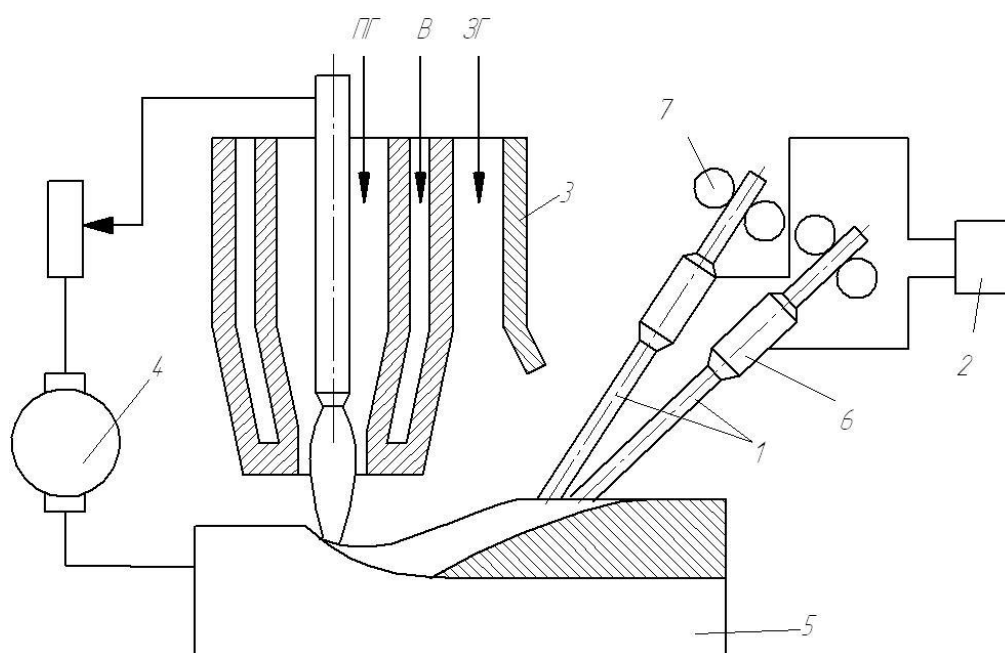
Схема выполнения плазменной наплавки двумя проволоками
